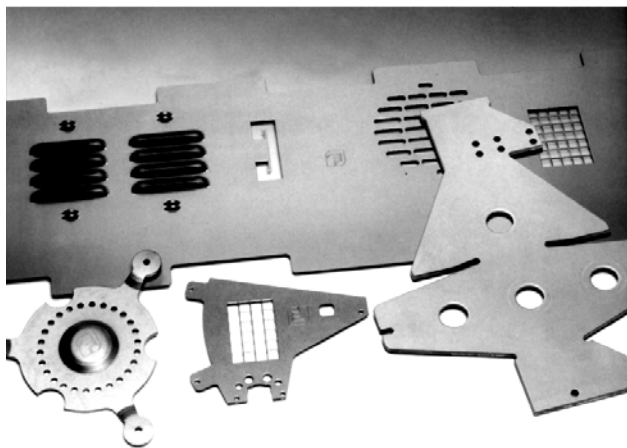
Образцы деталей, штампуемых на револьверных координатно-пробивных прессах
